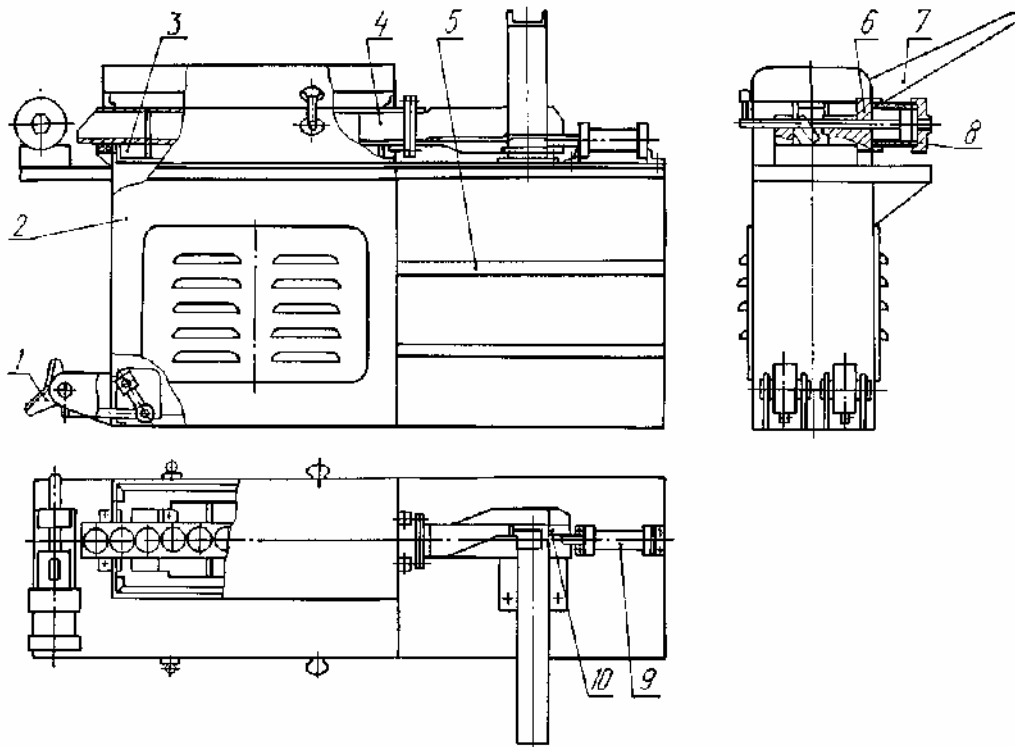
Стенд для сборки шатунно-поршневой группы: 1 – педальный привод; 2 – корпус; 3 – нагреватель; 4 – лоток; 5 – стеллаж; 6 – пресссборочный механизм; 7 – питатель; 8 и 9 – пневмоцилиндры; 10 – отсекатель
